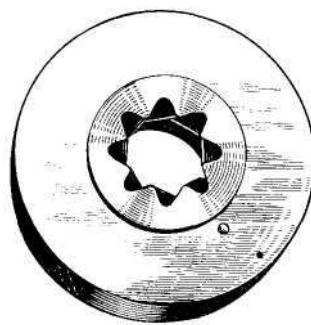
Приспособление для снятия конического упорного подшипника главной передачи
